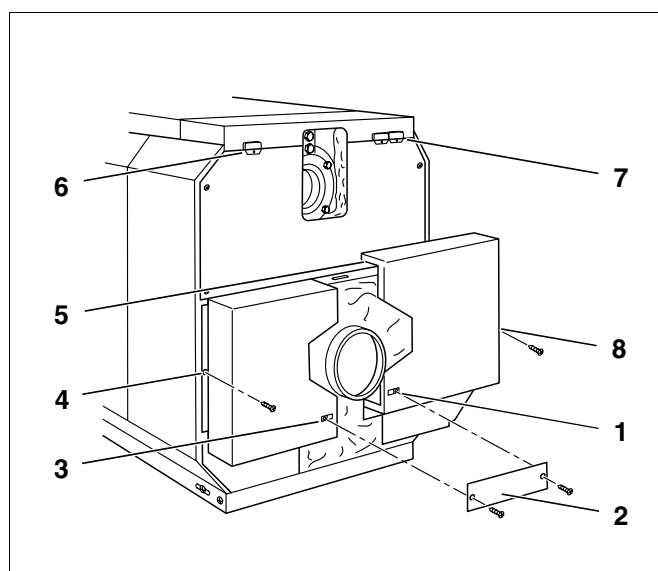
Montage - éléments de la paroi arrière de la chaudière
